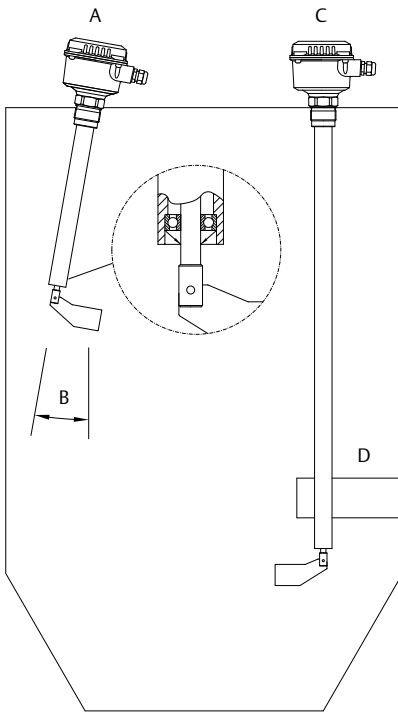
mostra como o interruptor de nível deve ser montado.
